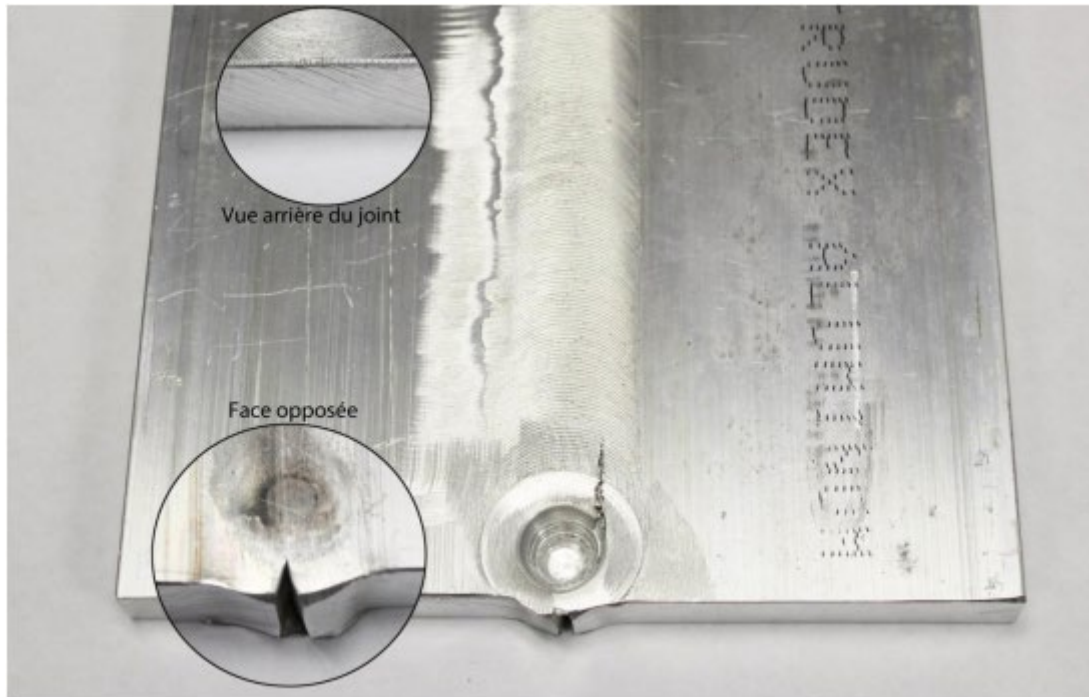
Échantillon de plaque de 12.7 mm (1/2 pouce) soudée en une seule passe [8] [3]
